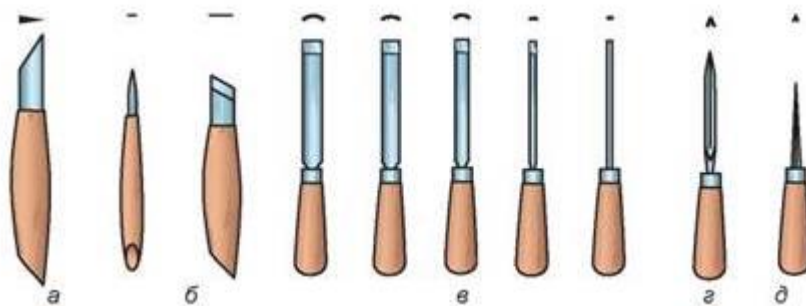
Інструменти для геометричного різьблення: а - різак; б - косий ніж; в - напівкруглі стамески; г - кутова стамеска; д - шило
